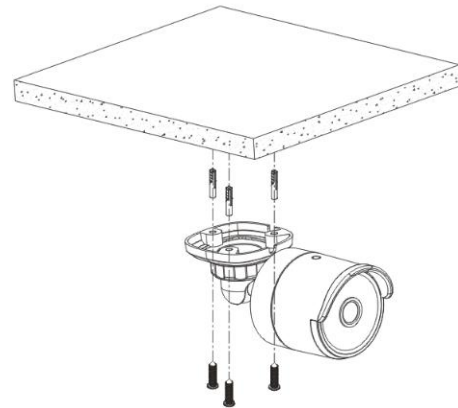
a Installazione a soffitto per telecamere bullet.
